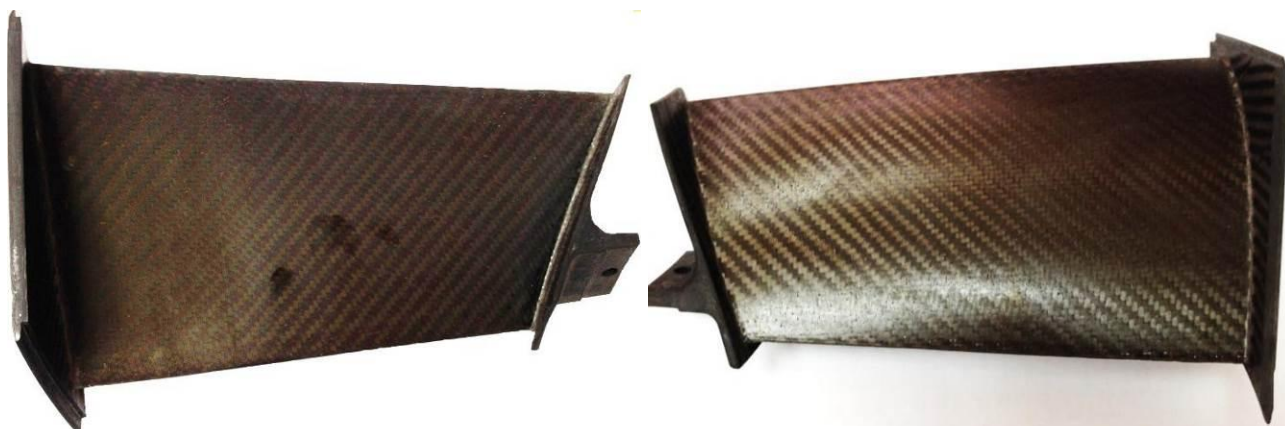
Опытный образец направляющего аппарата первой ступени компрессора низкого давления из углепластика БМИ-3/03692
